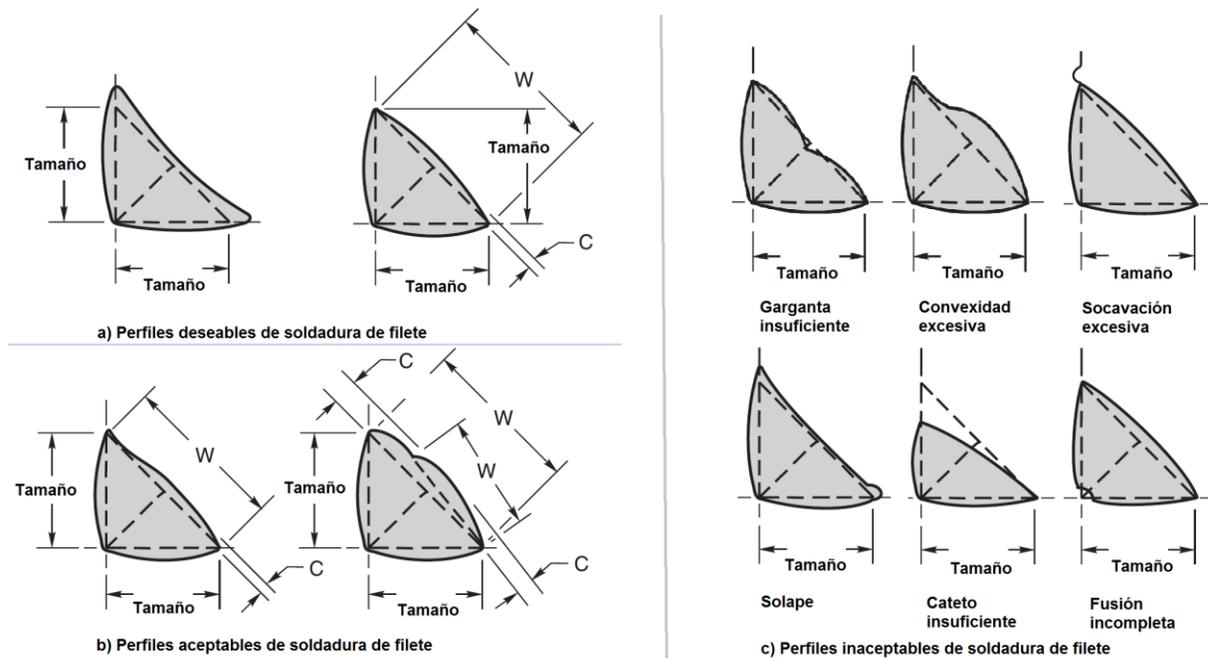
Perfiles aceptables e inaceptables de soldadura de filete.
